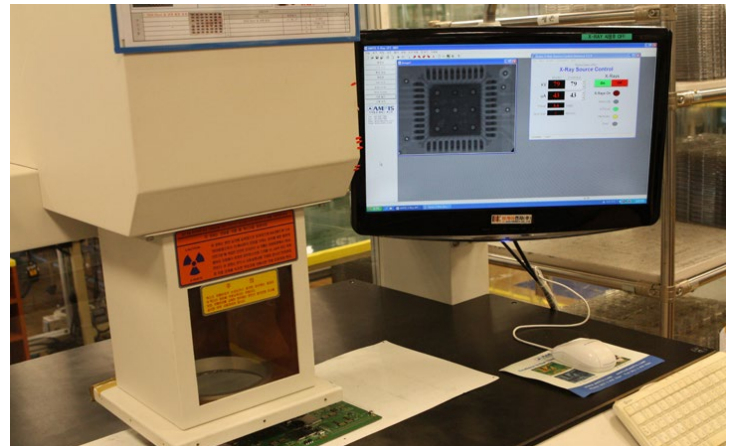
Inspección por rayos X para comprobar la calidad de la soldadura
